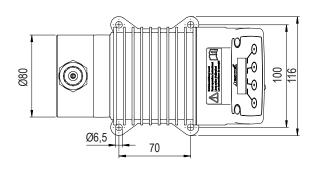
Габаритный чертеж MAGDOS LK/LP с дозирующей головкой из нержавеющей стали (1.4571) (все размеры в мм)
